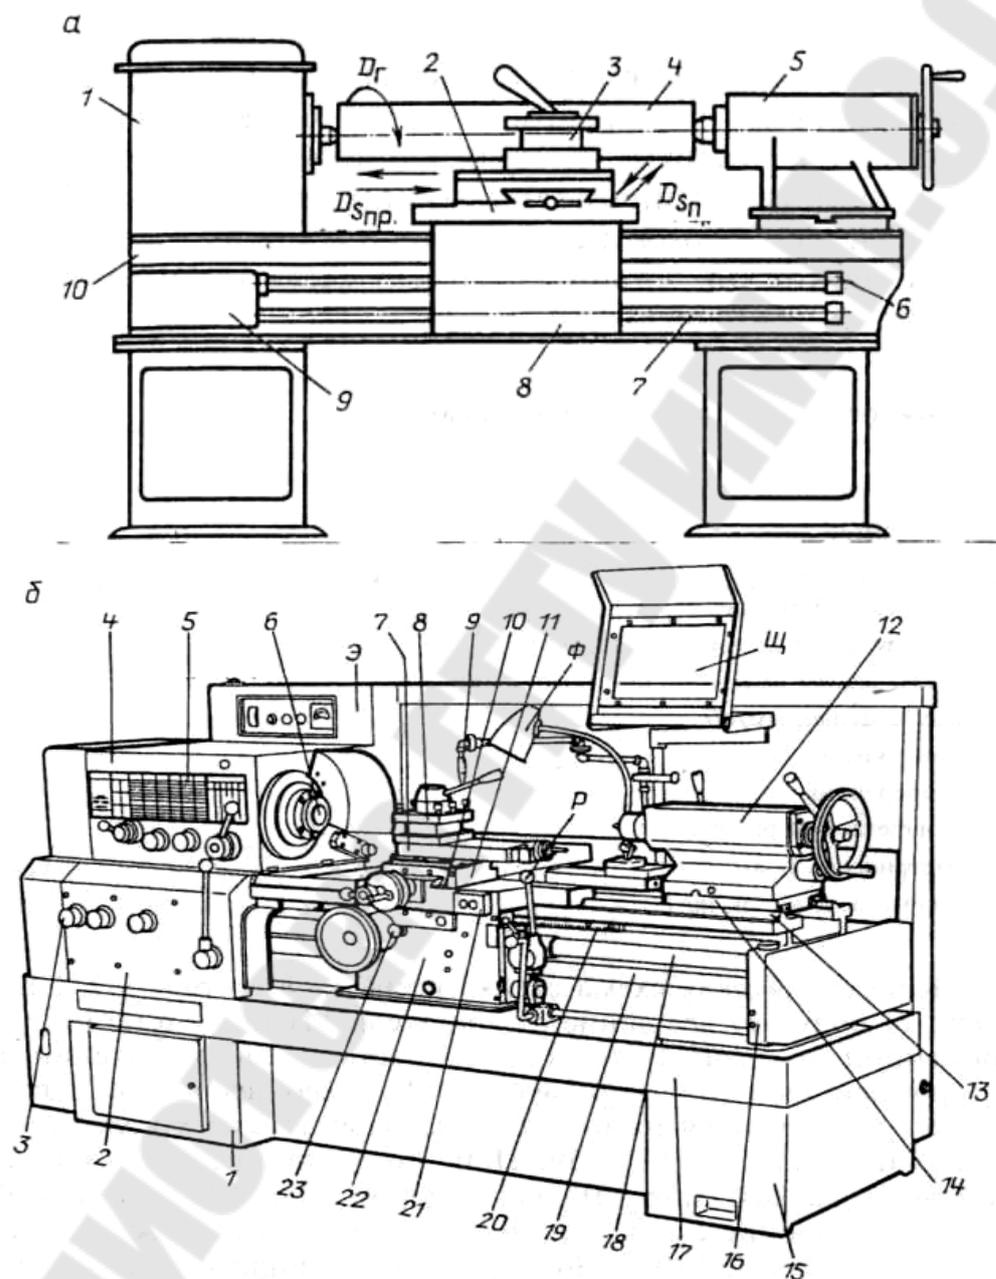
Схема токарно-винторезного станка (а) и общий вид станка мод. 16К20 (б)
